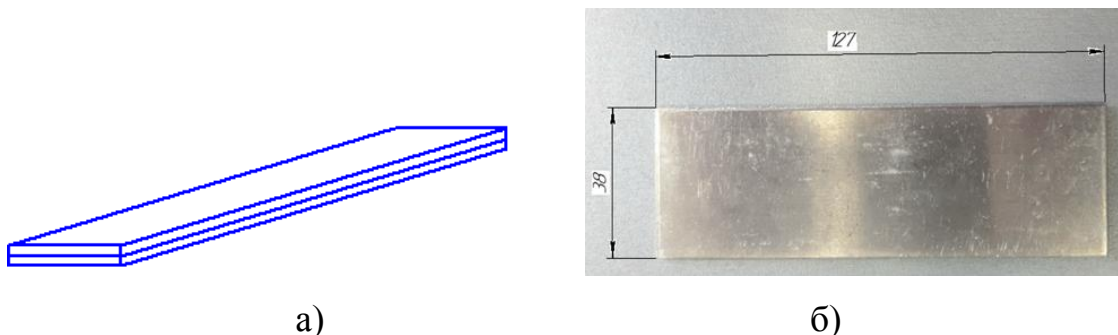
Схема расположения образцов (а) и размеры образца (б)
